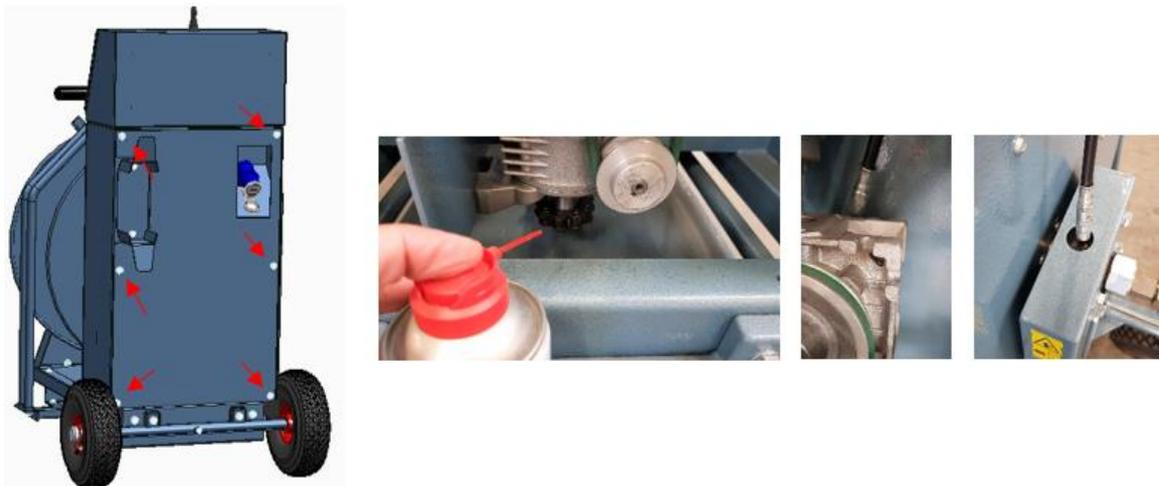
; Ingrassaggio della guida della catena e dei cuscinetti del tamburo
